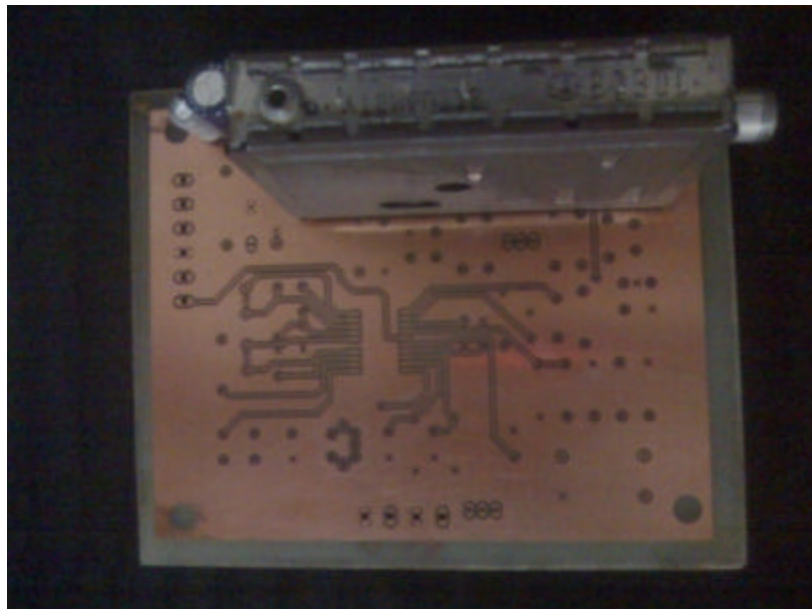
Vista superior de PCB después de soldar el sintonizador y algunos condensadores.
